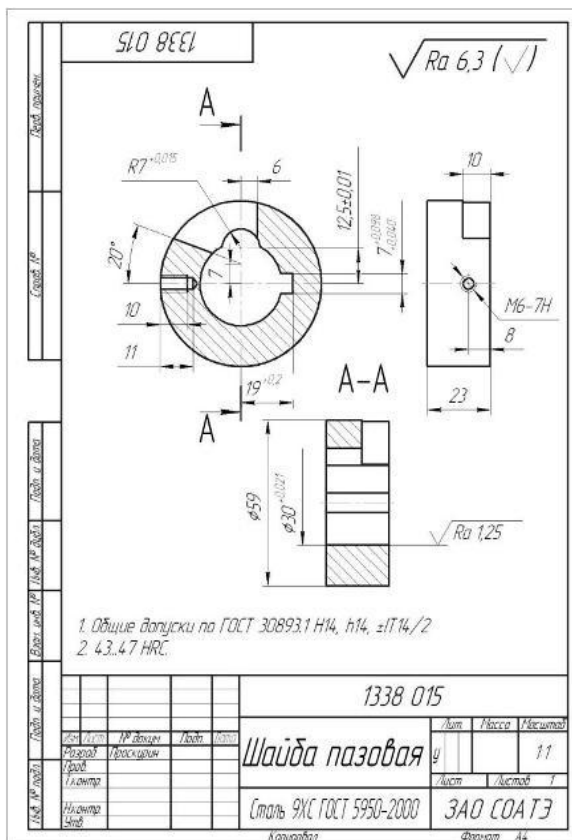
Деталь испытательного стенда. Шайба пазовая
